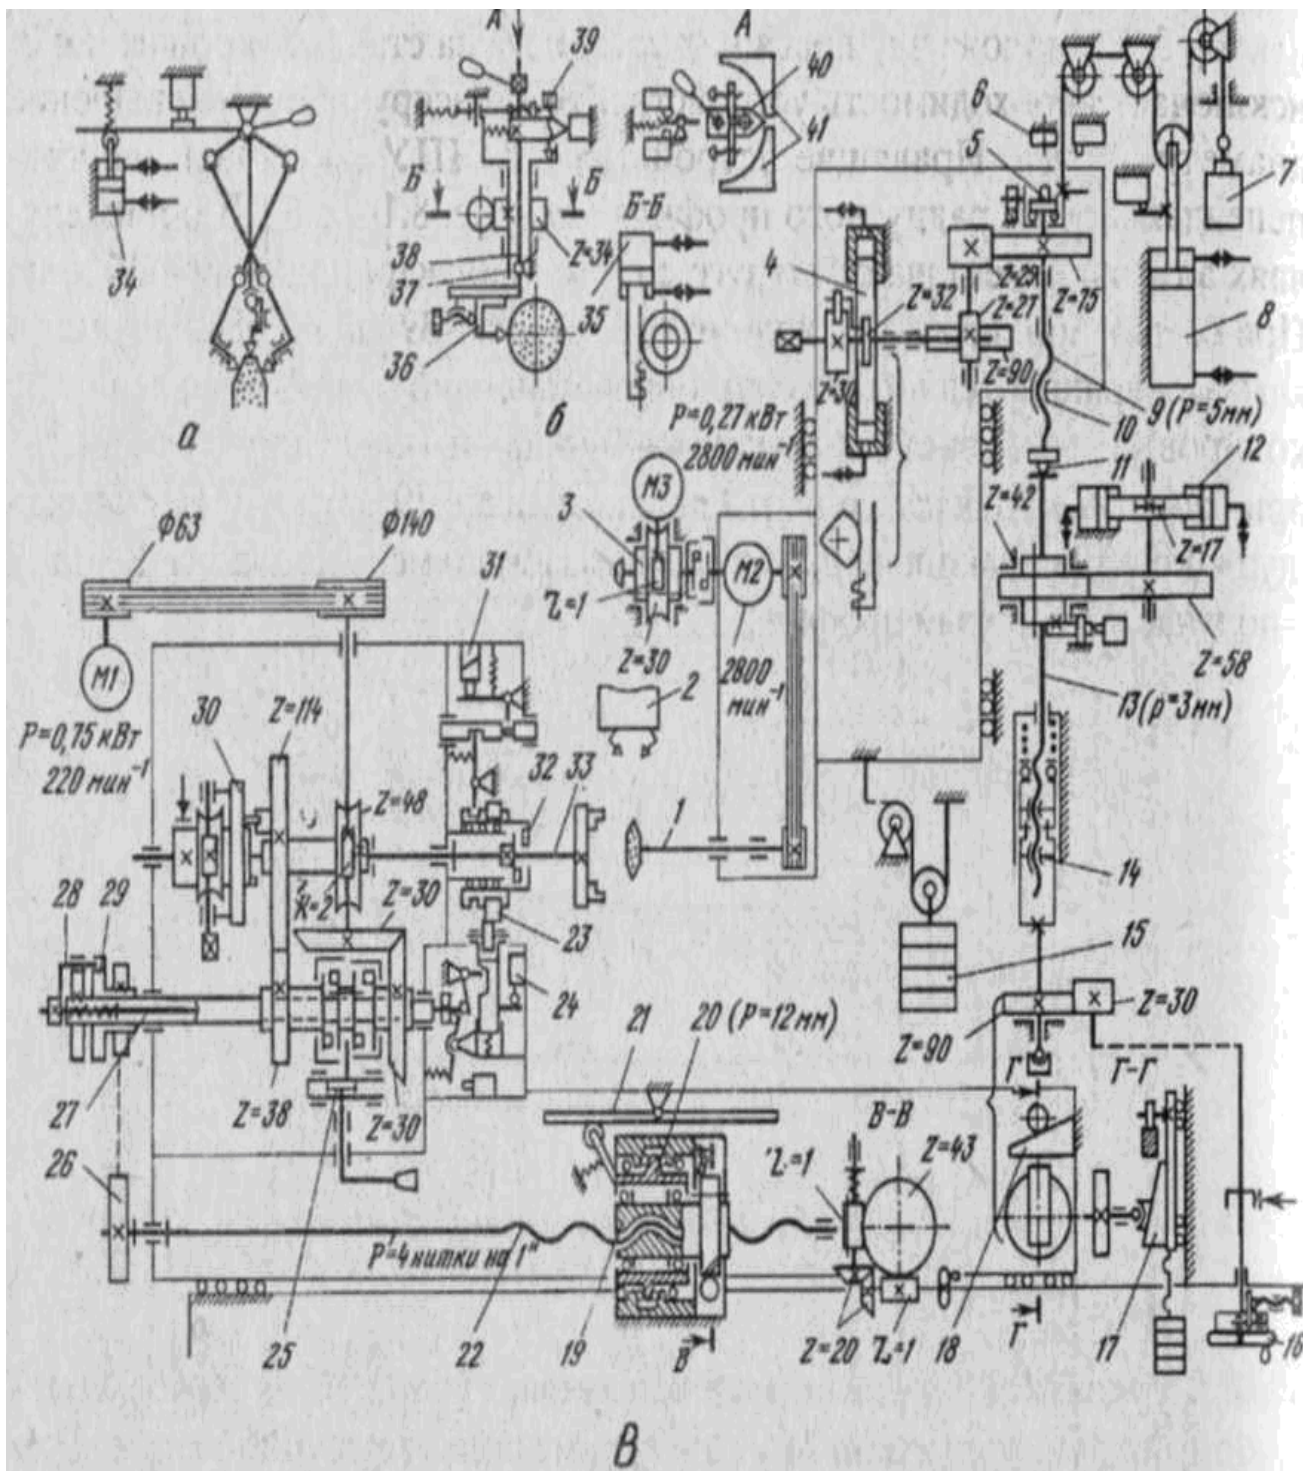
Кинематическая схема внутрирезьбошлифовального станка.
